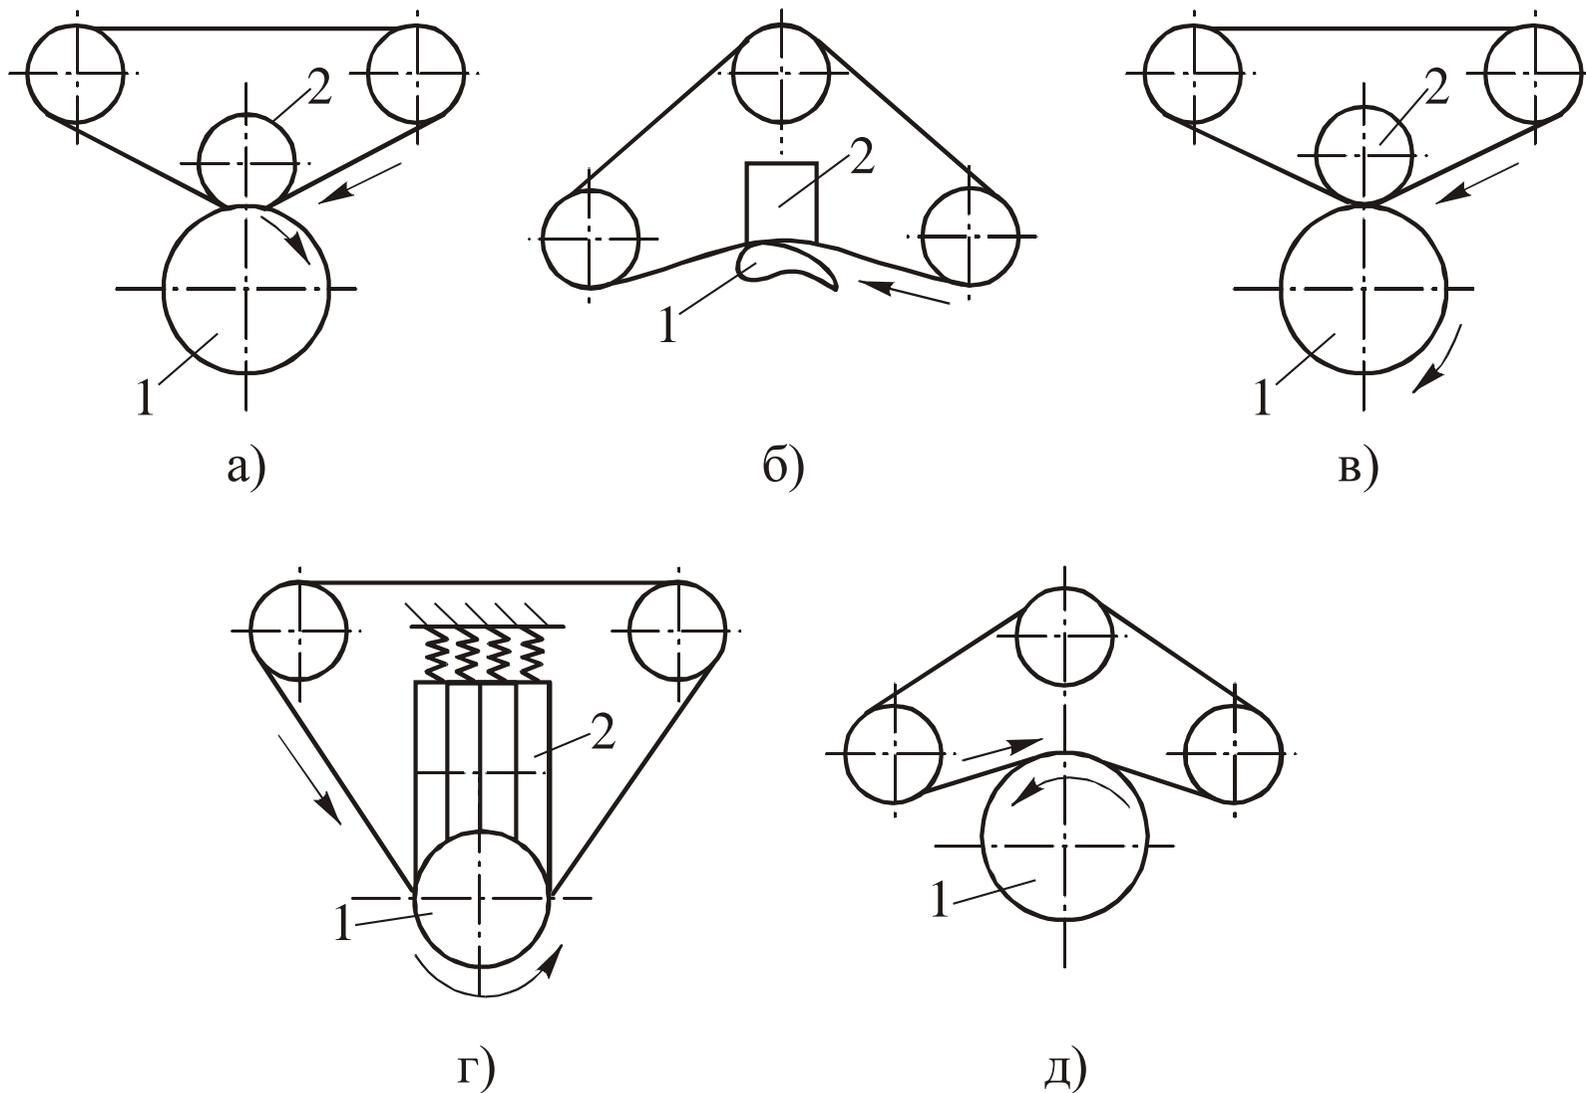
Схемы обработки заготовок абразивными лентами:
